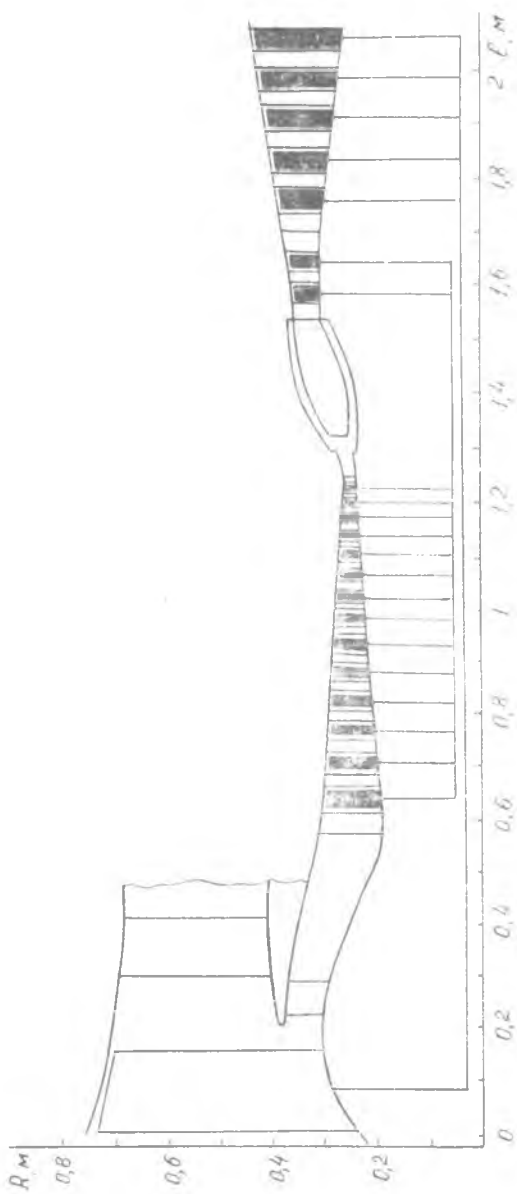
Меридиональный профиль лопатки турбокомпрессора двухлопастного ТР₂ЛД
